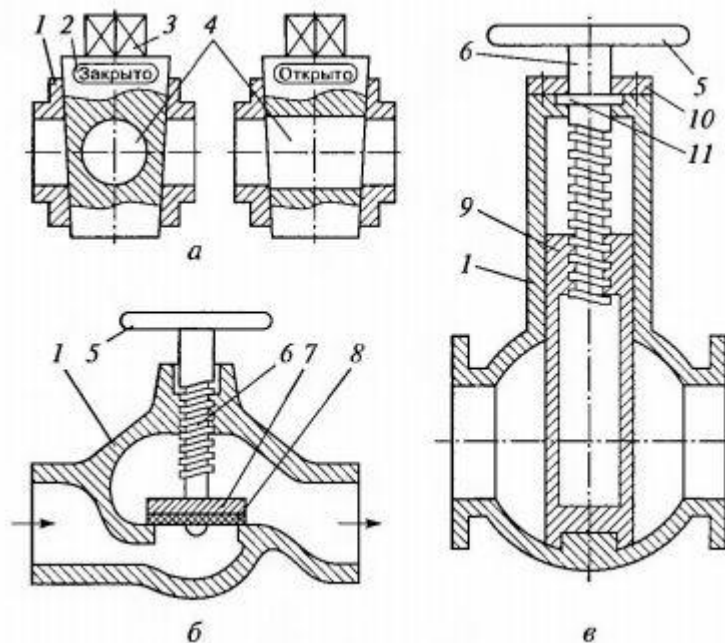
Водопроводная арматура: а - пробковый кран; б - вентиль; в - задвижка; 1 - корпус; 2 - поворотная пробка; 3 - головка; 4 - проходное отверстие; 5 - маховик; 6 - шпindelь; 7 - клапан; 8 - прокладка; 9 - задвижка; 10 - крышка; 11 – буртик.
